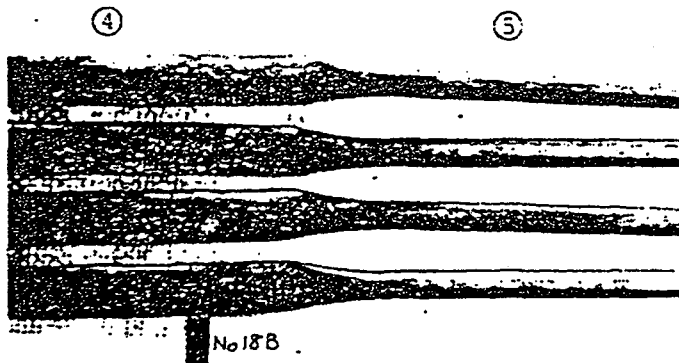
Farklı çok-yarma haddeleme basamaklarında parçanın üç tane üst görünüşünü gösterir.
